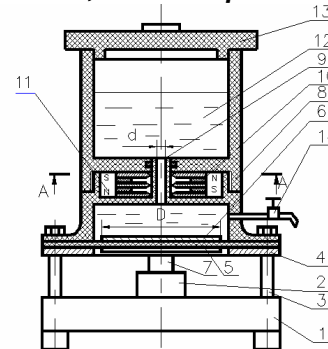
Конструктивна схема кавітаційно-магнітного пристрою для обробки води: 1 – основа; 2 – вібропривід; 3 – стійки; 4 – пластина; 5 – мембрана; 6 – диски; 7 – шток; 8 – ванна; 9 – отвір; 10 – загострені пластини; 11 – магніти; 12 – вода; 13 – кришка; 14 – кран
